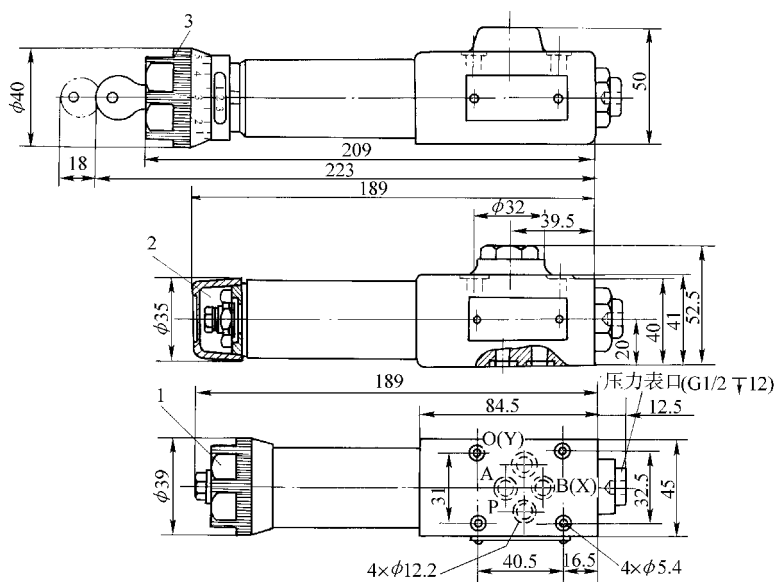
DZ6DP 型直动式顺序阀外形尺寸
